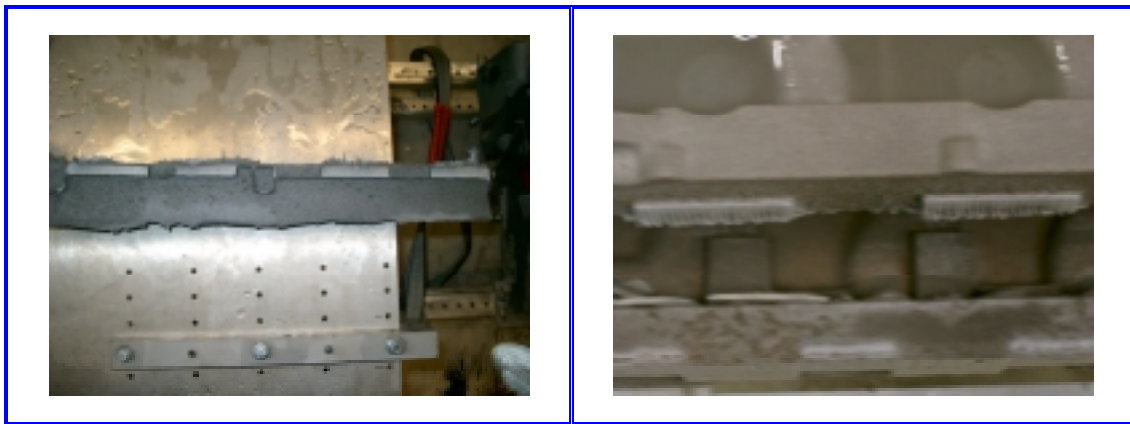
Cortes de colada en Block V6 DC 3.5 Lts mediante maquinado hidroabrasivo.
